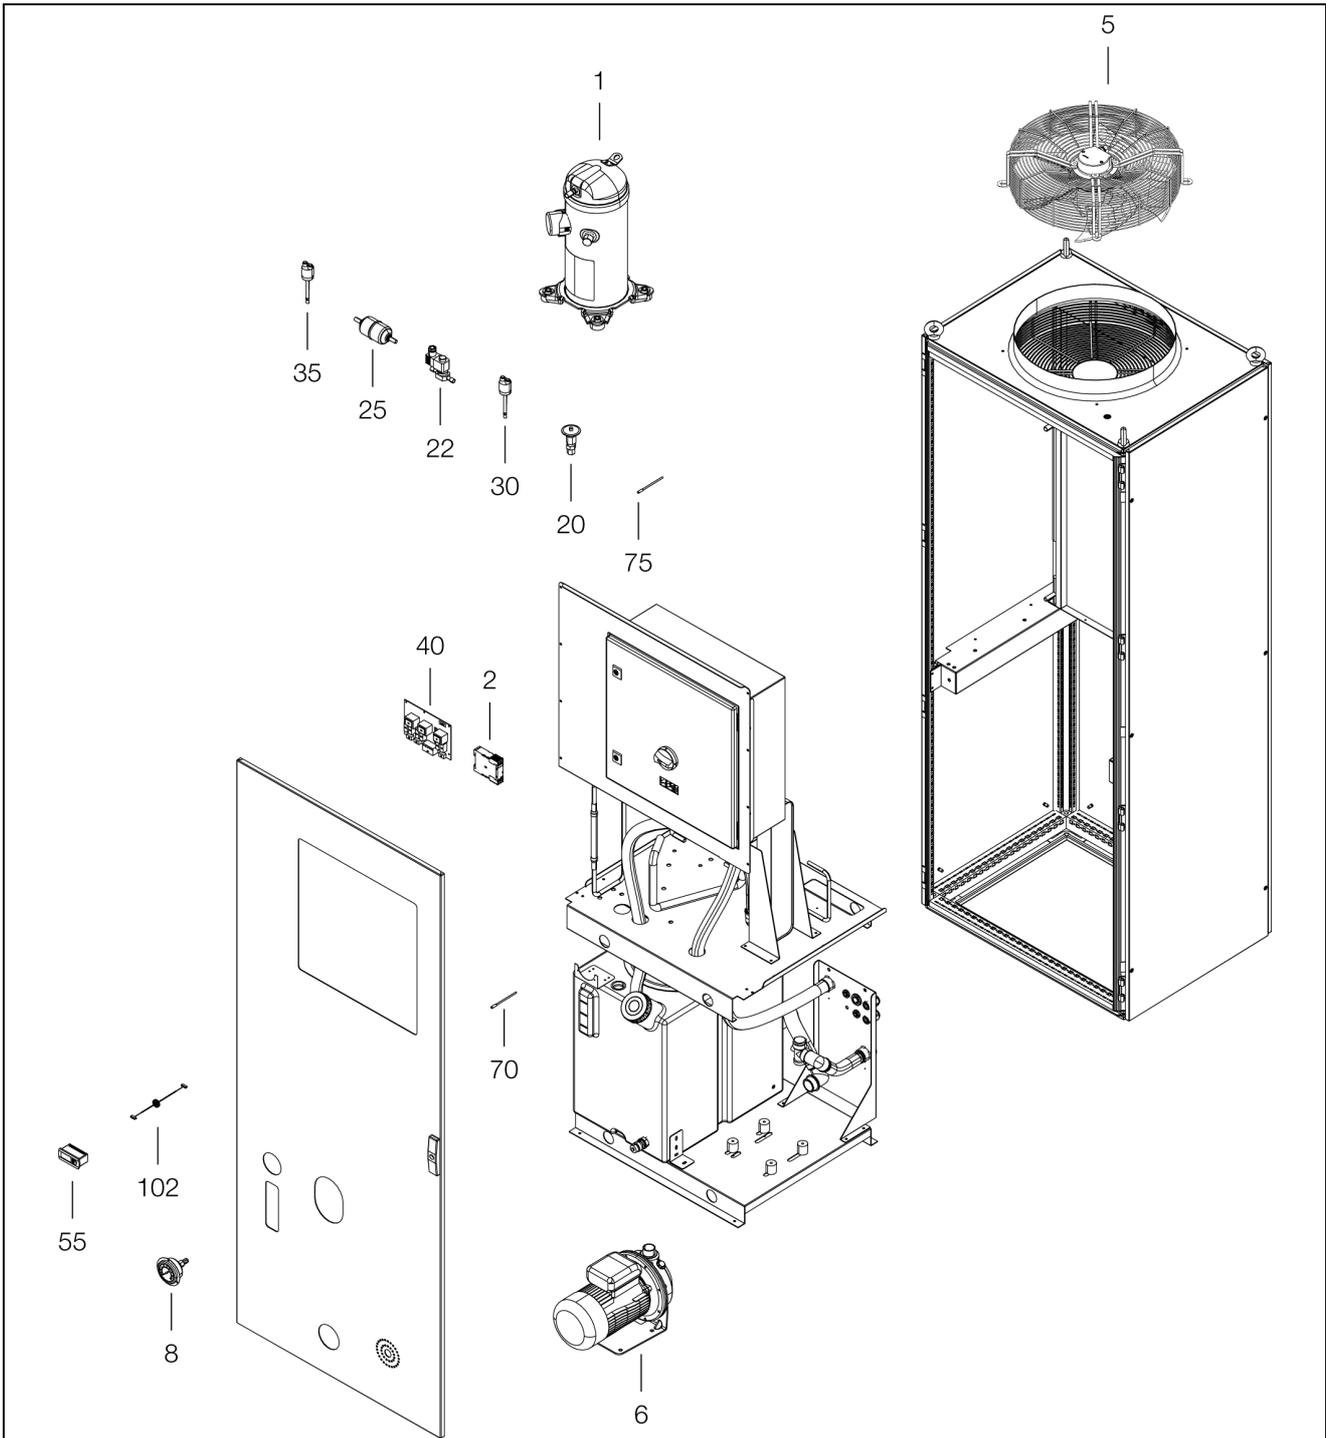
Ersatzteilzeichnung Typen 3335.790, 3335.830, 3335.840, 3335.850
